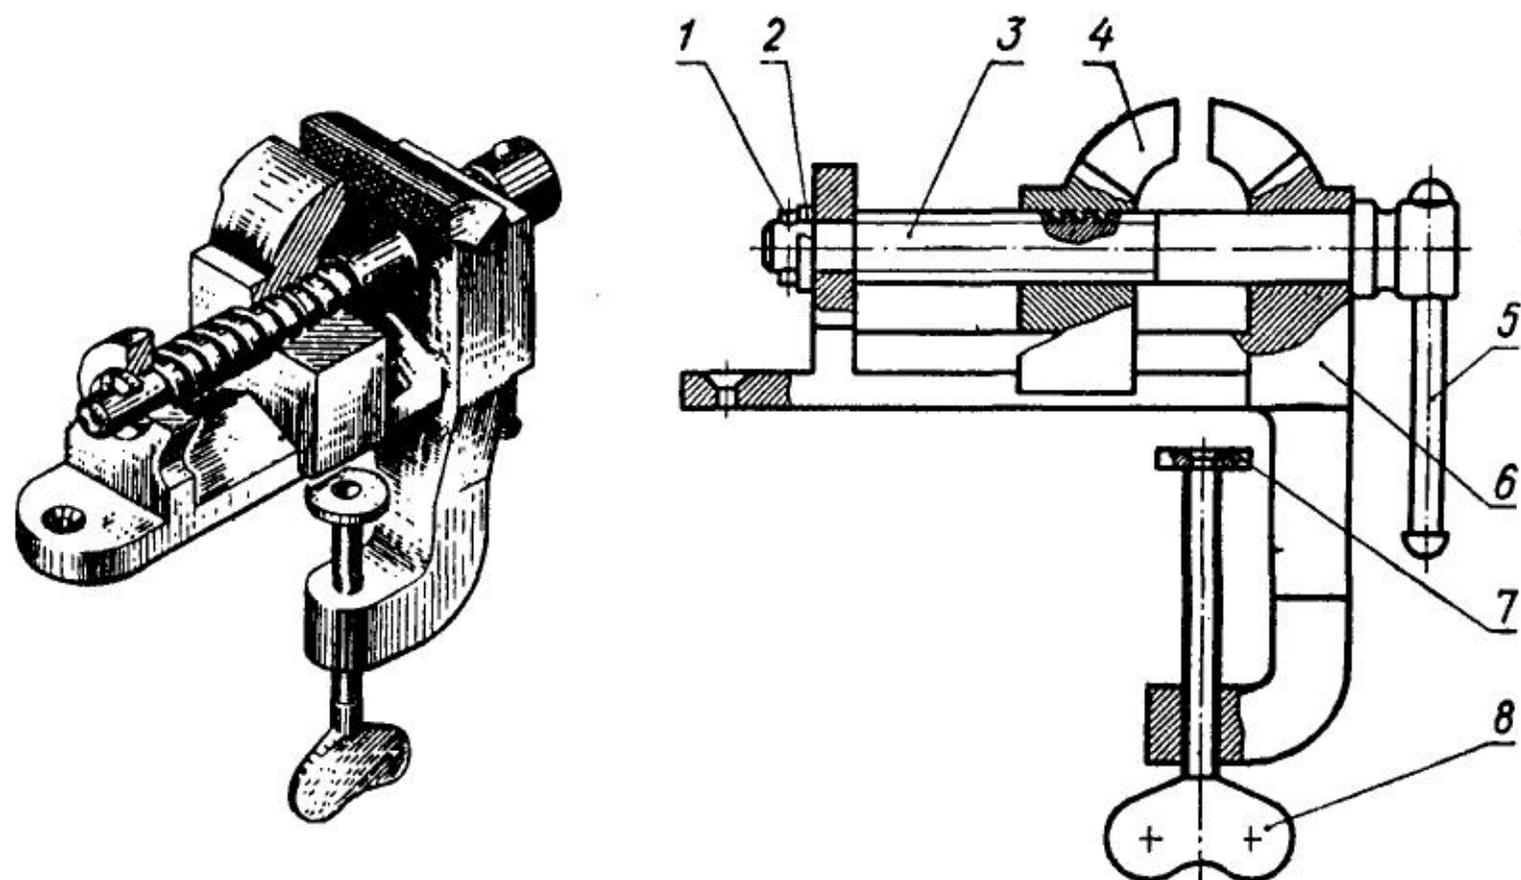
Лещата слюсарні: 1 — штифт; 2 — шайба; 3 — гвинт ходовий; 4 — губка рухома; 5 — руків'я; 6 — губка нерухома; 7 — шайба; 8 — гвинт.
